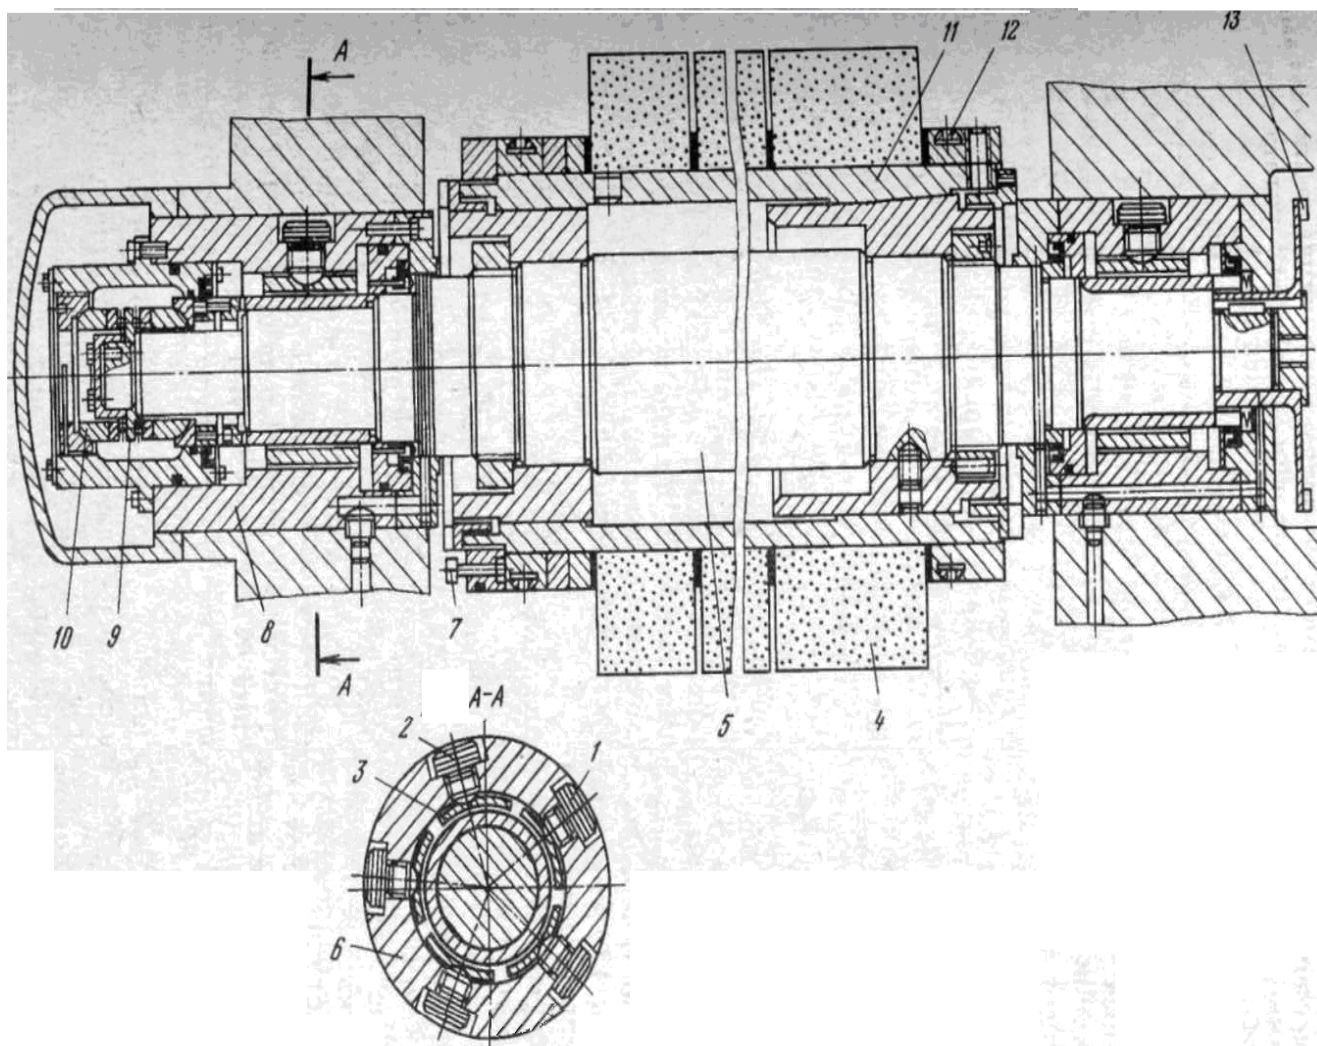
Шпиндель бесцентрового круглошлифовального станка с широким кругом: 1 – винт со сферической головкой, 2 – колпачки защитные, 3 - вкладыши, 4 – широкий шлифовальный круг, 5 – шпиндель, 6, 8, - обоймы подшипников, 7 – винты крепления подшипников, 9 – упорные под-
